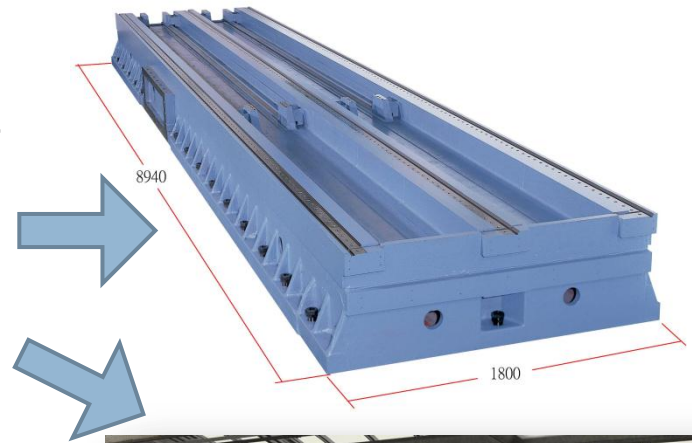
Станина горизонтально-фрезерного обрабатывающего центра H50 на заводе-изготовителе TAJMAC-ZPS (Чехия)
